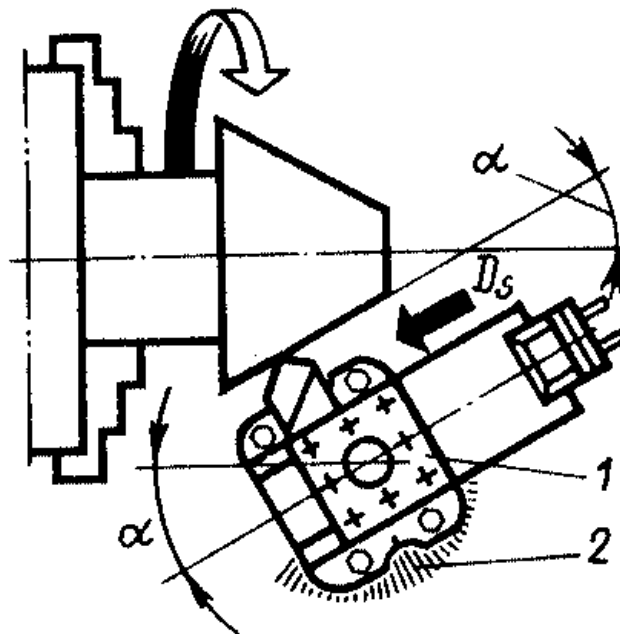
Схема обработки наружной конусной поверхности способом поворота верхней части суппорта:
